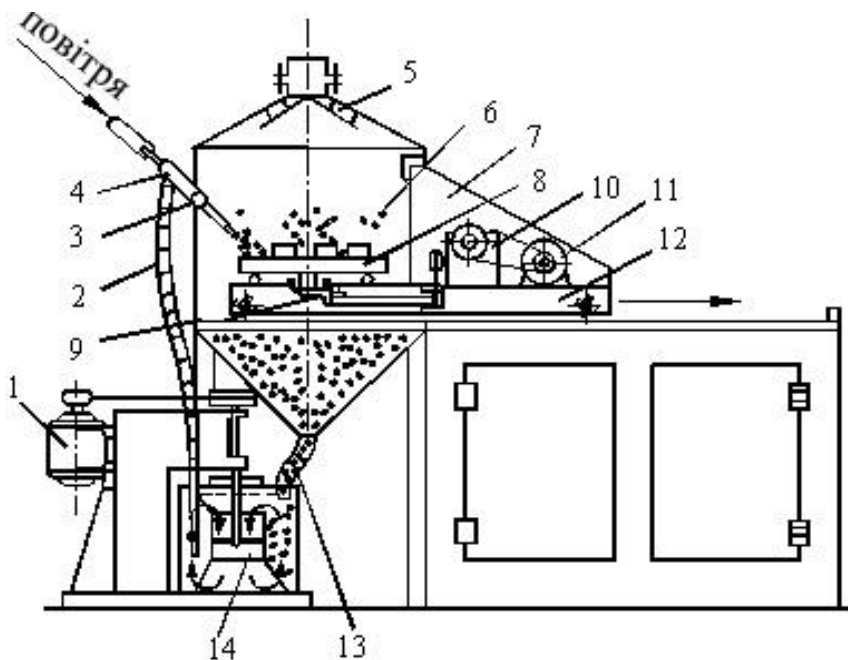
Установка, що працює за принципом ежектування абразивної суміші: 1 і 11 – електродвигуни; 2 і 13 – шланги; 3 – кувальова опора; 4 – струминний апарат; 5 – відбивач; 6 – камера; 7 – кожух; 8 – поворотний стіл; 9 – конічна передача; 10 – редуктор; 12 – візок; 14 – мішалка
